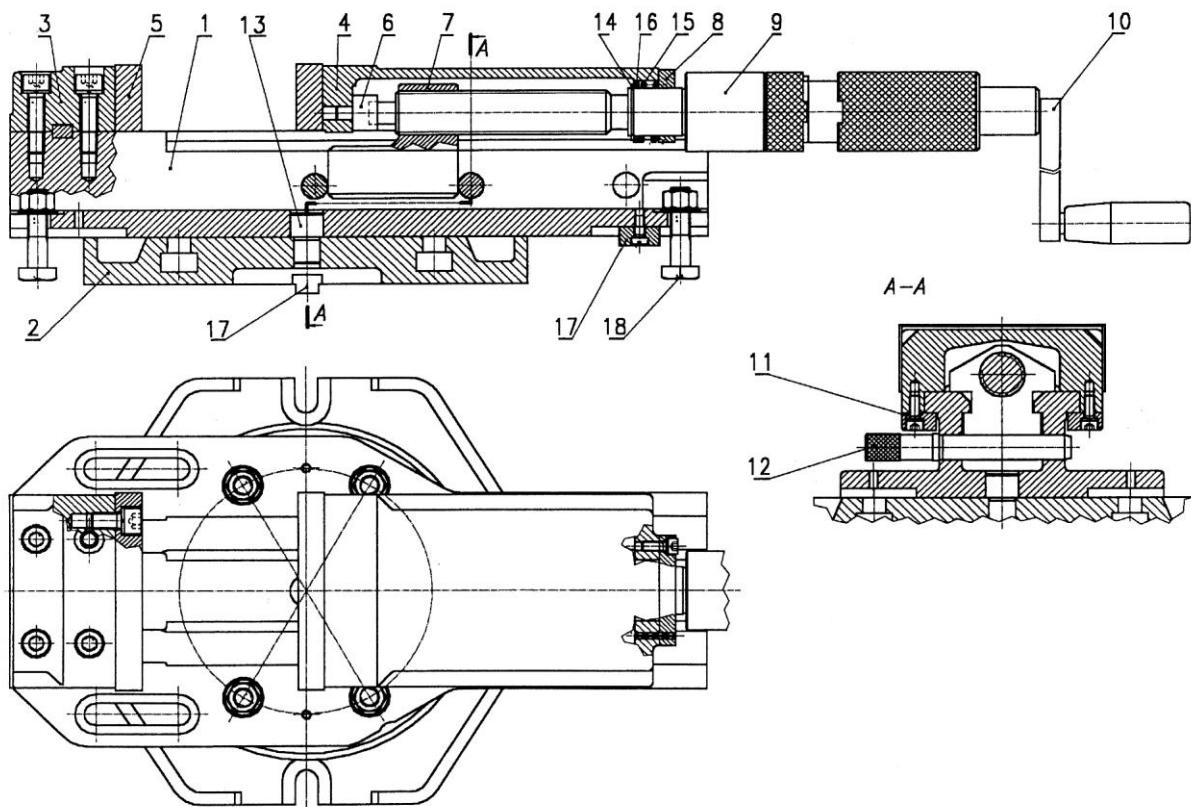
Aufbau des Schraubstocks 6516-M mit 6585 Sockel.
